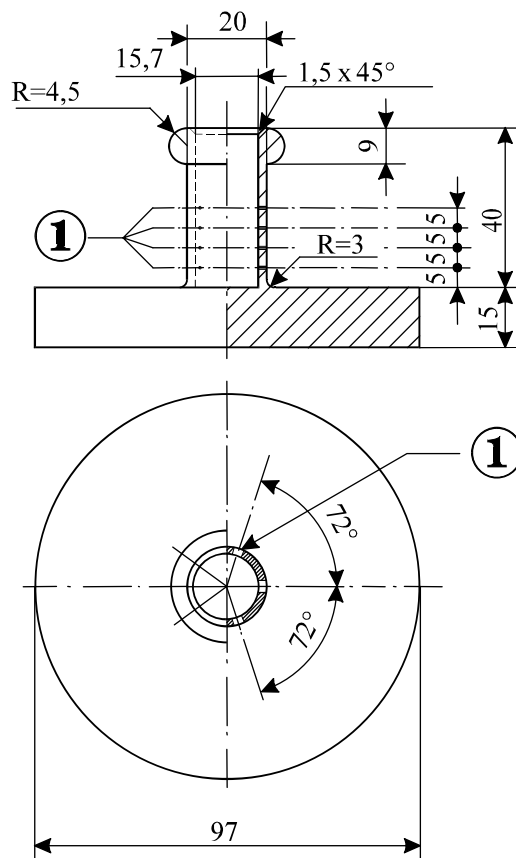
Hohlter Bronzeyylinder, einseitig verschlossen
